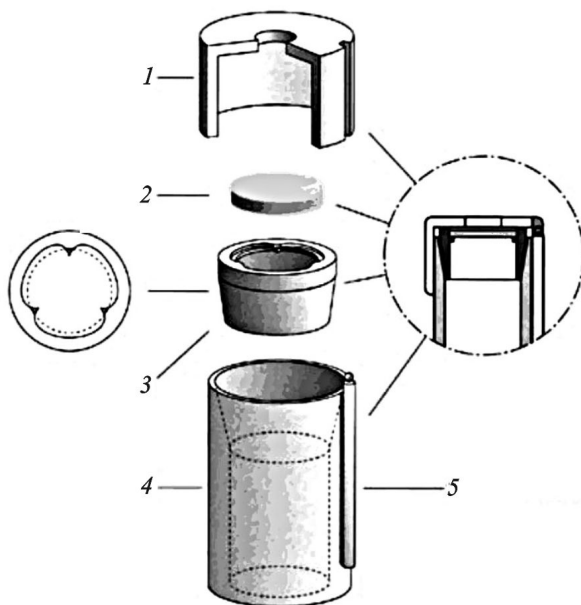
Конструкция держателя образца: 1 – крышка; 2 – образец; 3 – поддержка образца; 4 – трубчатый держатель образца; 5 – термопара образца
